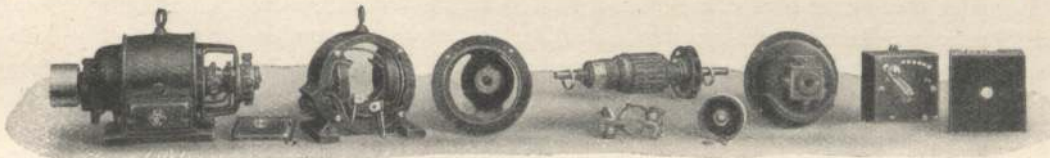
Der offene Gleichstrom-Nebenschluß-Motor und seine Einzelteile (mit luftgekühltem Anlasser).
